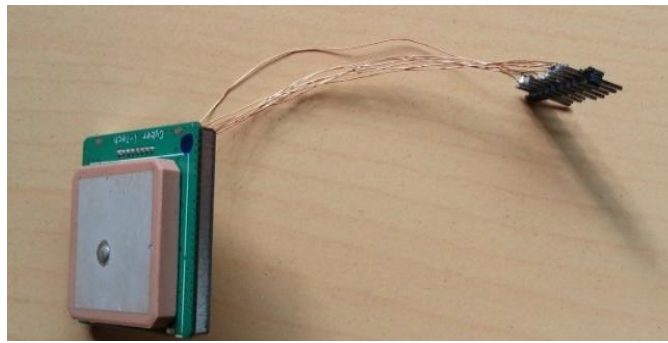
Soudage du module GPS ST32 Skytraq
